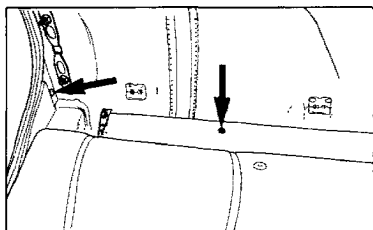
Расположение нижних отверстий для крепления ремня на автомобиле с левым расположением руля
